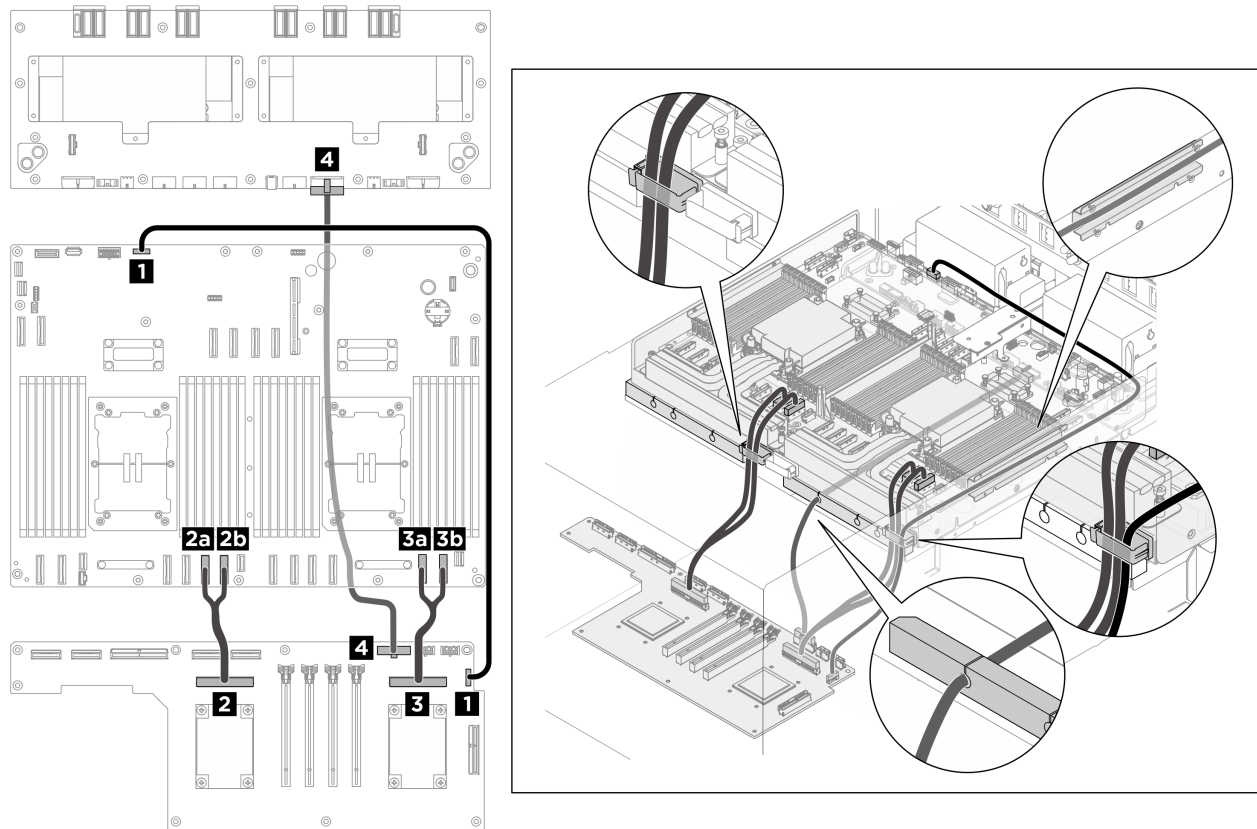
Kabelführung für PCIe-Switch-Platine
